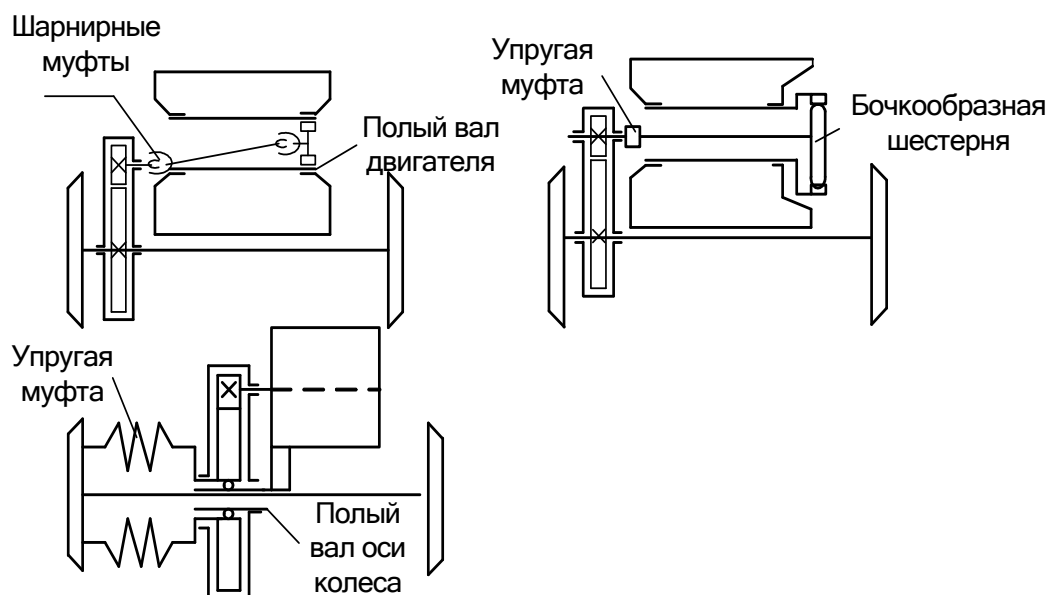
Схема опорно-рамного подвешивания тяговых двигателей
